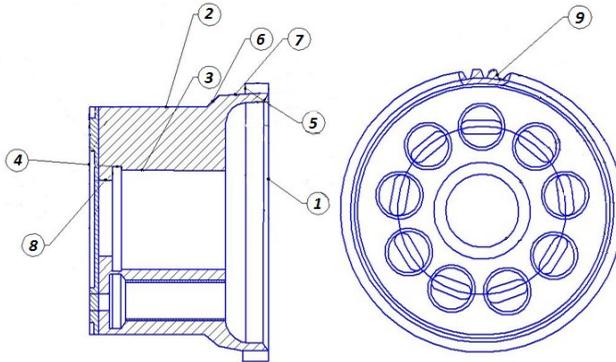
Корпусная деталь с нумерацией поверхностей: 1, 4, 5 – торцы детали, 2 и 7 – внешние цилиндрические поверхности, 3 и 8 – поверхности внутренних отверстий, 6 – конусная поверхность, 9 – канавки сложной формы
